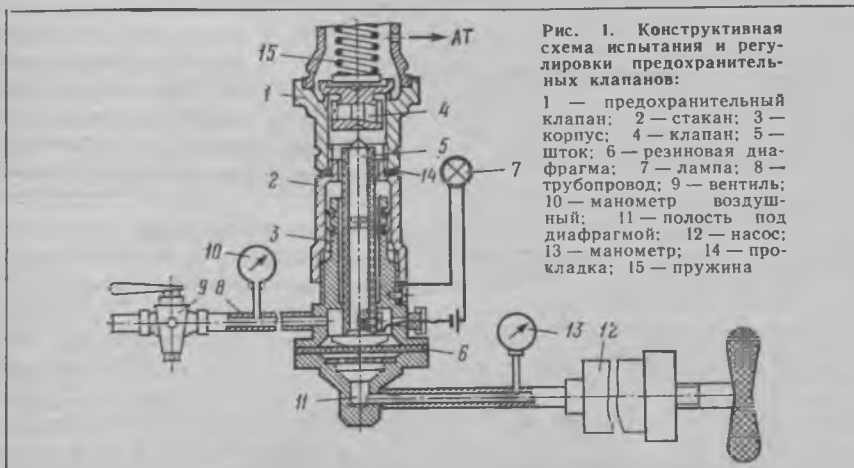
Конструктивная схема испытания и регулировки предохранительных клапанов:
